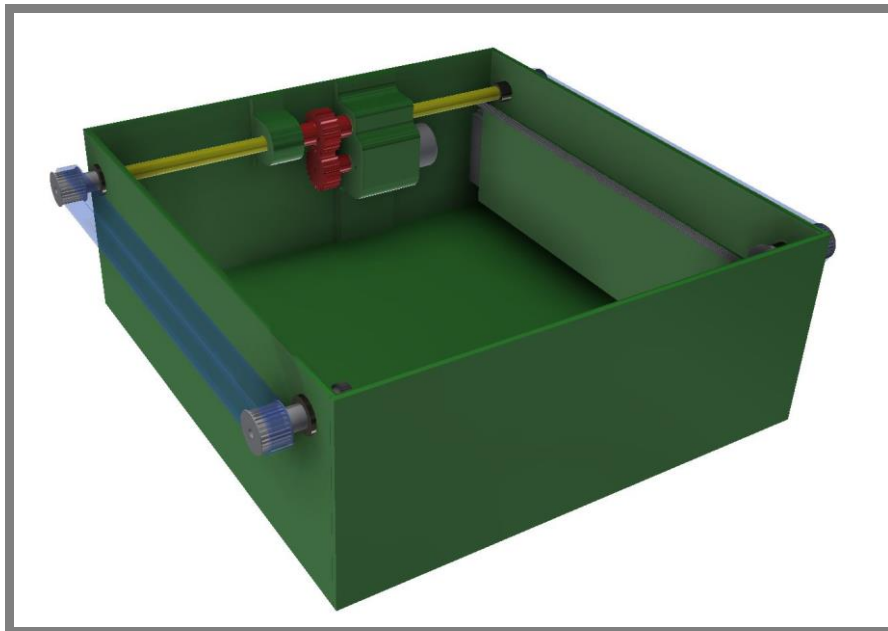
Třetí varianta vysouvacího mechanismu
